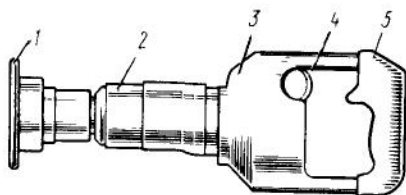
Монтажный поршневой пистолет ПЦ-84: 1 — прижим, 2 — муфта, 3 — коробка с механизмом накола, 4 — спусковой механизм, 5 — рукоятка
